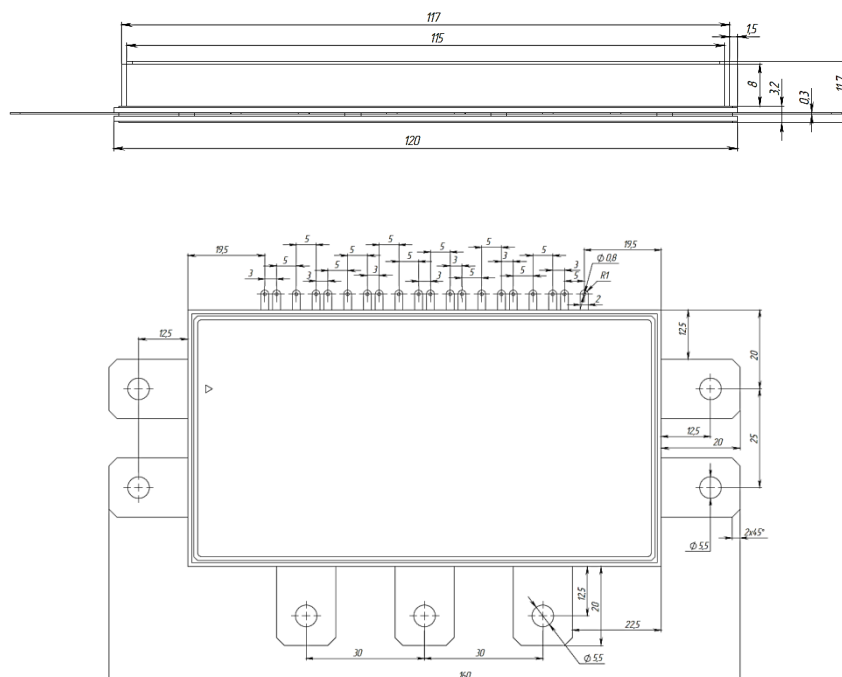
Габаритные, присоединительные и установочные размеры модулей:
